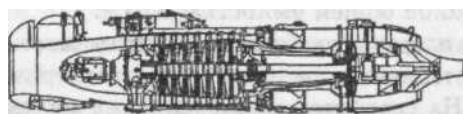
Турбореактивный двигатель BMW-003 [59]
